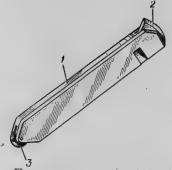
1 — корпус; 2 — нож; 3 — ролик
